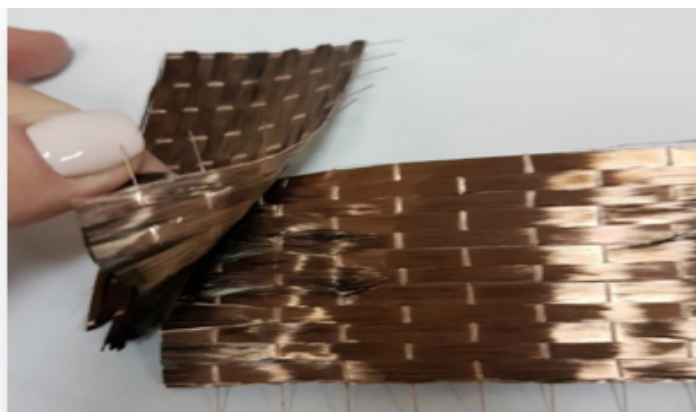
Схема расположения точек скрепления ультразвуковой сваркой
